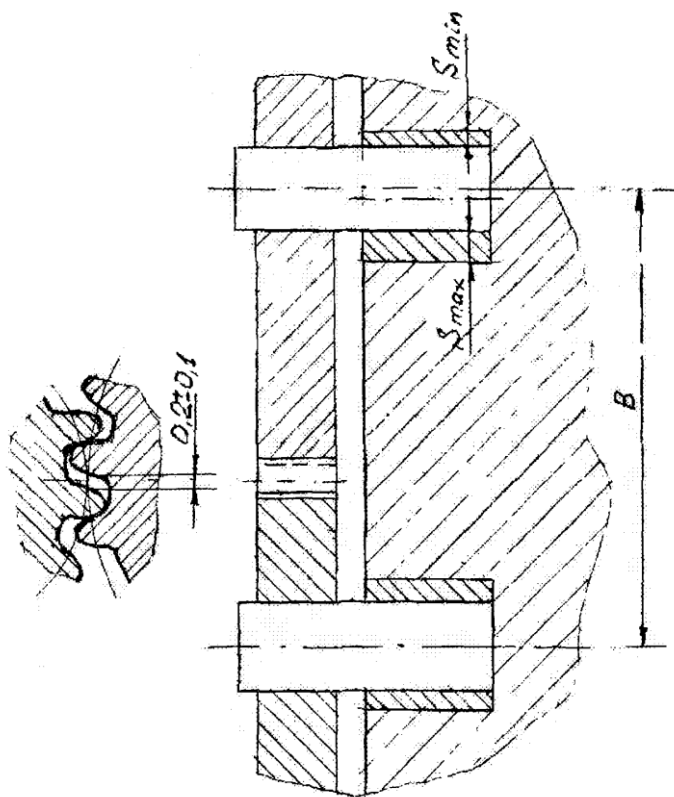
5 – Схема привода механизма газораспределения двигателя АШ – 62ИР
